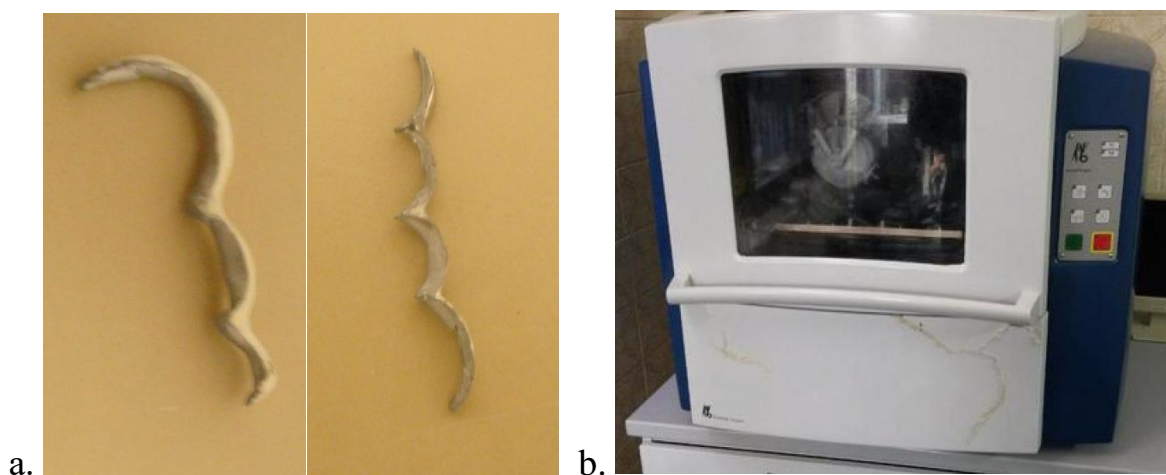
а Стабілізуєчі (шинуючі) дискретні конструкції множинних мезоструктур на імплантатах, виготовлені шляхом фрезерування способом; б. CAD/CA.
